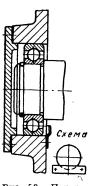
«Порог», улавливающий и удерживающий смазку в корпусе подшипника
